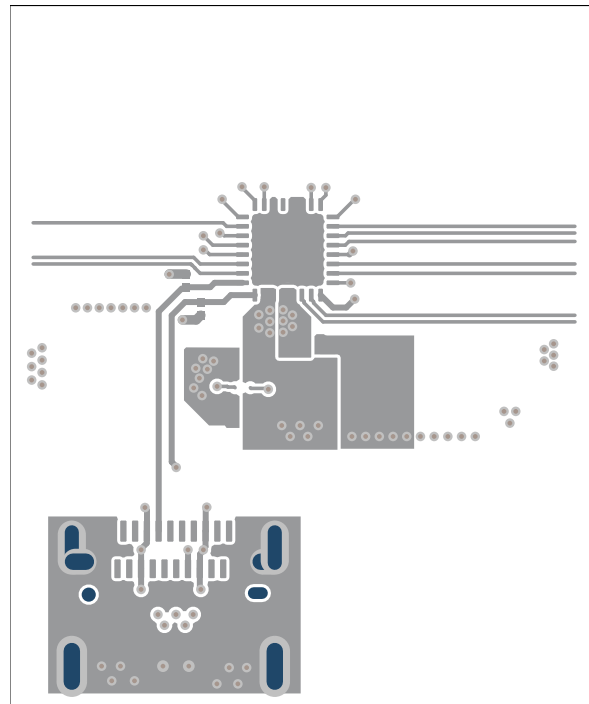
TPS25751S PCB Layout - Top Layer Routing
